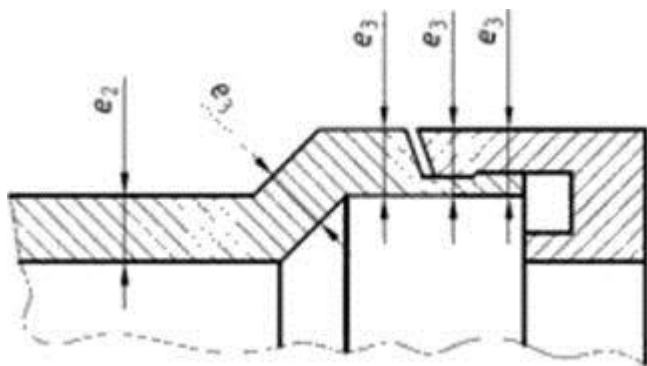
Толщина стенки раструба с крышкой для установки уплотнительного кольца
